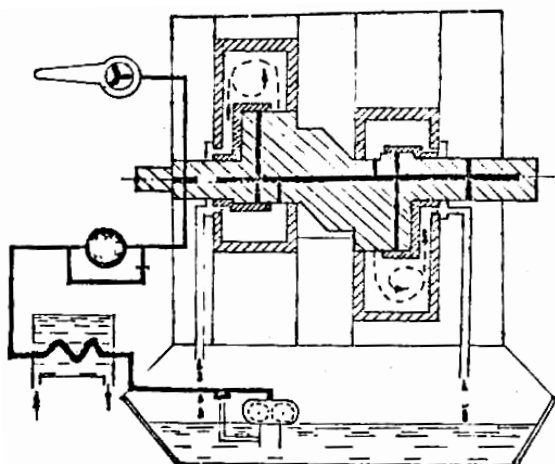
Схема смазочная и охлаждения ротора РПД
